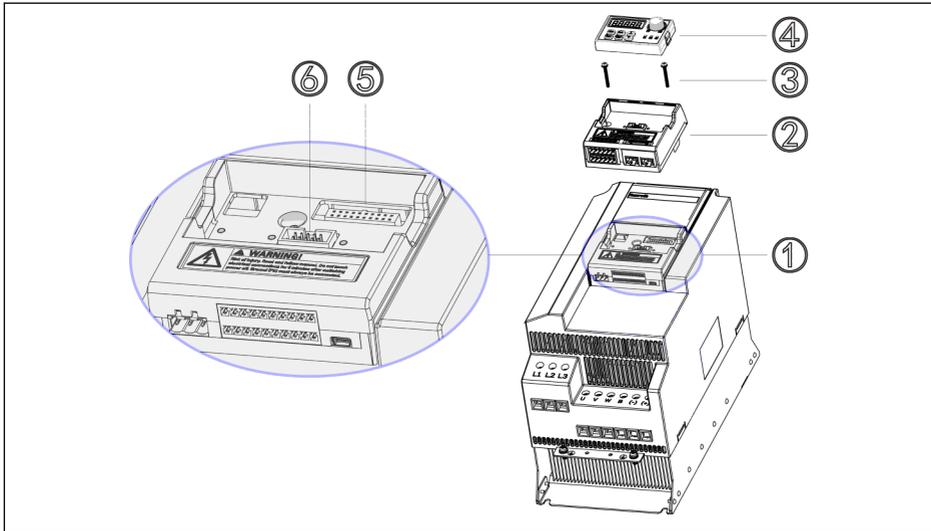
Montaje del módulo de tarjeta de extensión
